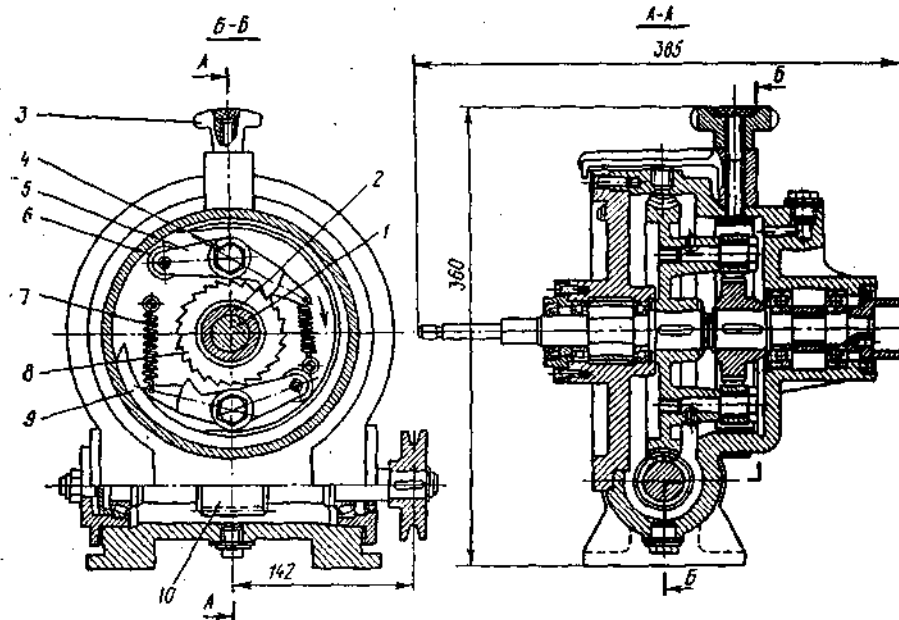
Редуктор привода дозатора борошна і води преса ЛПЛ-2М
